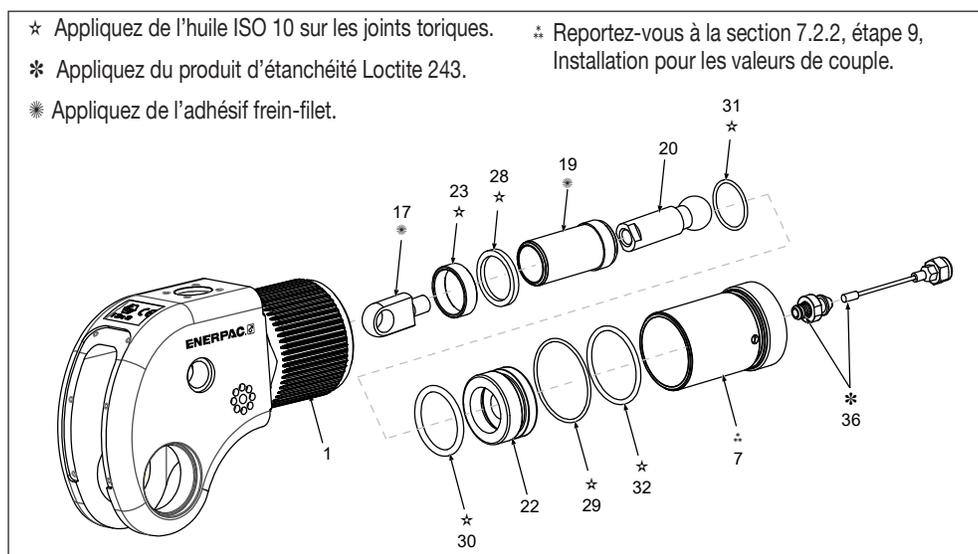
Vue éclatée des pistons DSX1500, DSX3000 et DSX5000
